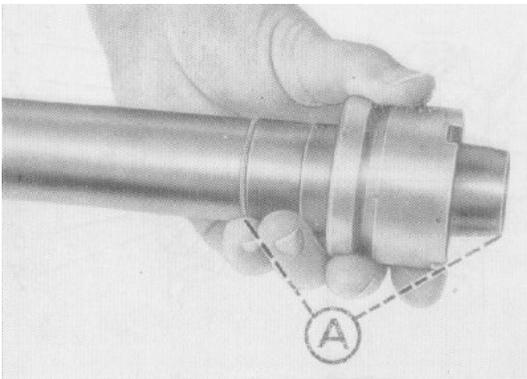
Aufschieben des Gewindinges (mit eingedrücktem Dichtring) auf das Führungsrohr mit Hilfe einer Montagehülse (A)
